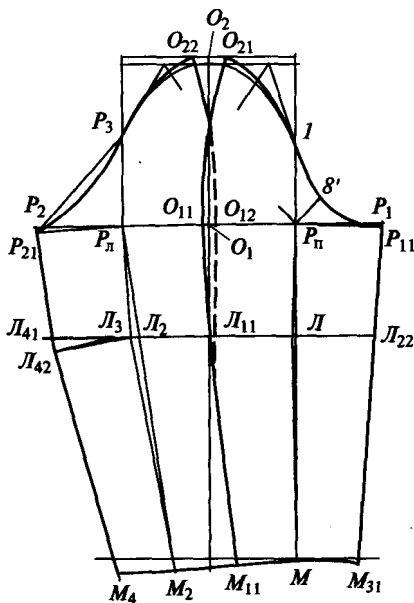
Чертеж конструкции двухшовного втачного рукава с верхним и нижним швами
